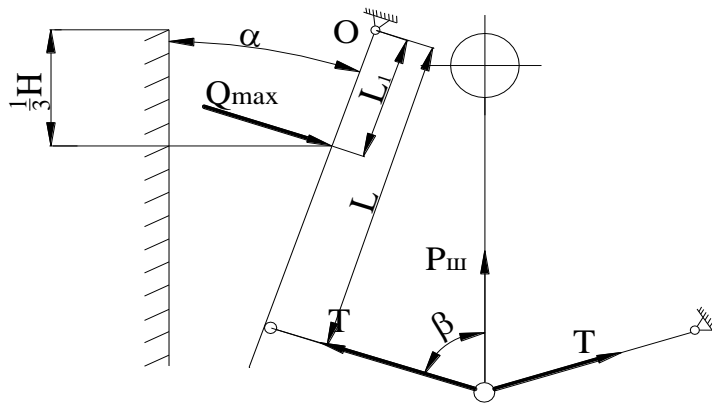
Розрахункова схема для визначення зусиль в деталях щокової дробарки з простим коливанням щоки
